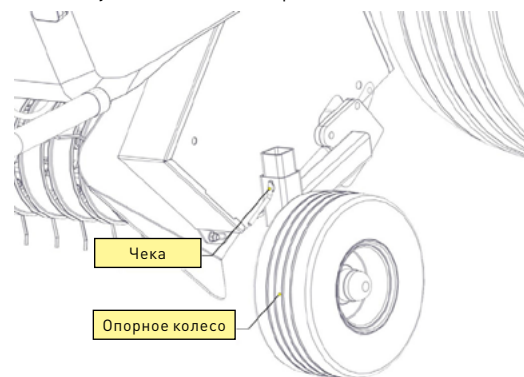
Регулировка рабочей высоты пресс-подборщика
